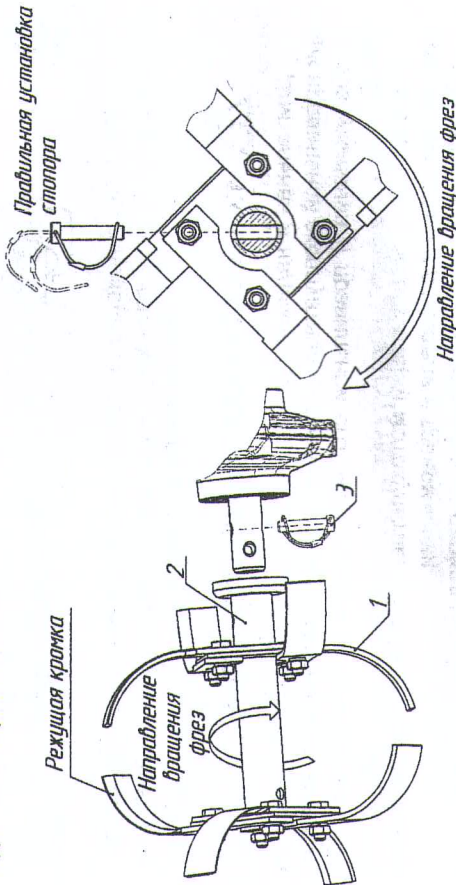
Установка 4-х фрез-культиваторов. 1 – фреза; 2 – культиватор двойной; 3 – стопор
